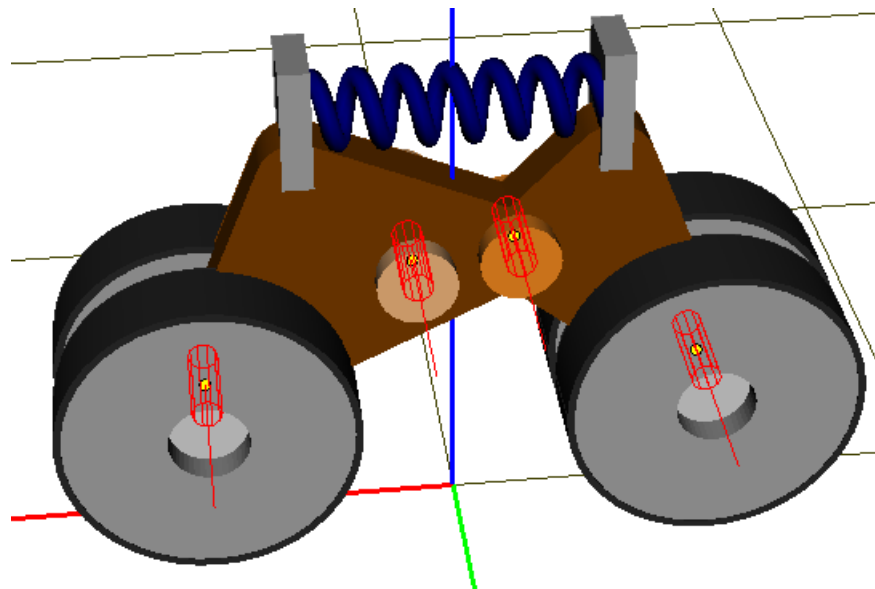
Шарниры балансирной подвески с двумя рычагами
